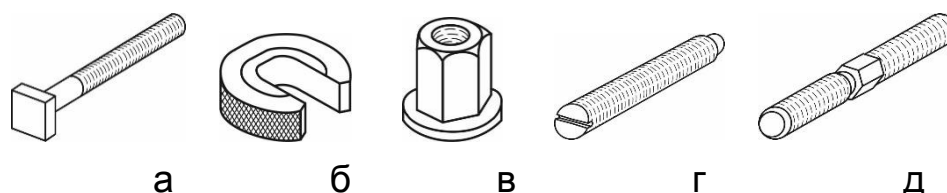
Примеры крепежных деталей: а – болт пазовый; б – шайба быстростъемная; в – гайка; г – винт; д – шпилька
